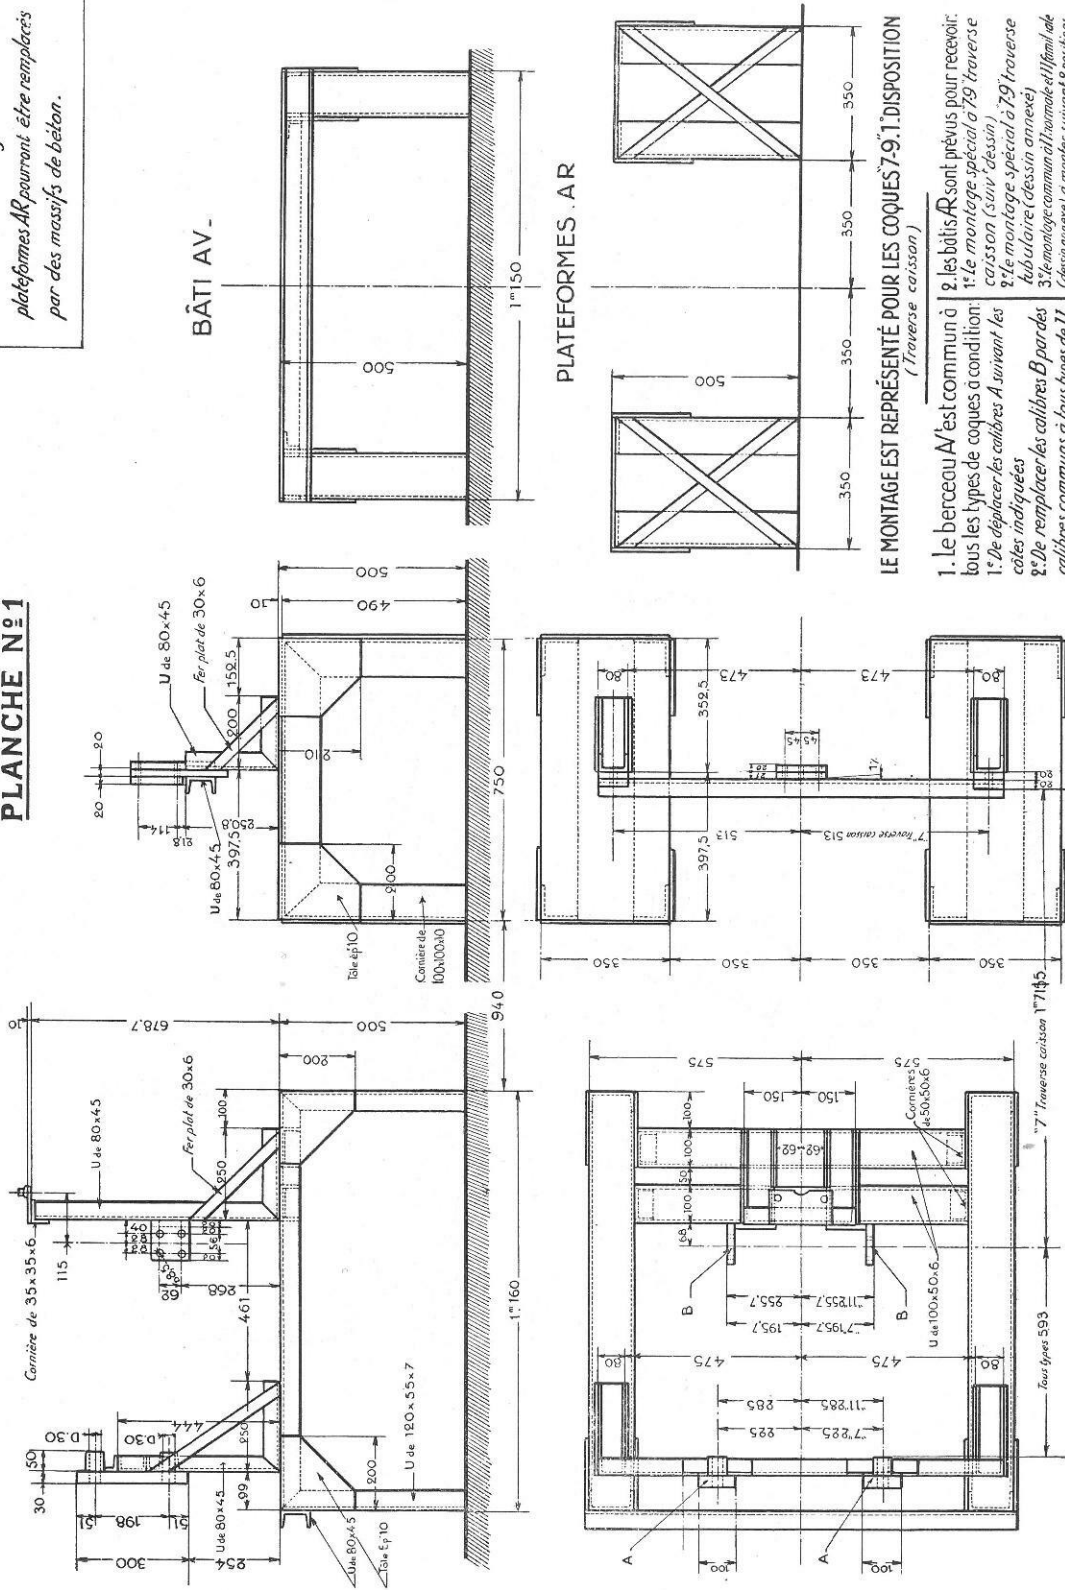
Plan de détail du montage de dégauchissage des carrosseries à traverse arrière caisson.
